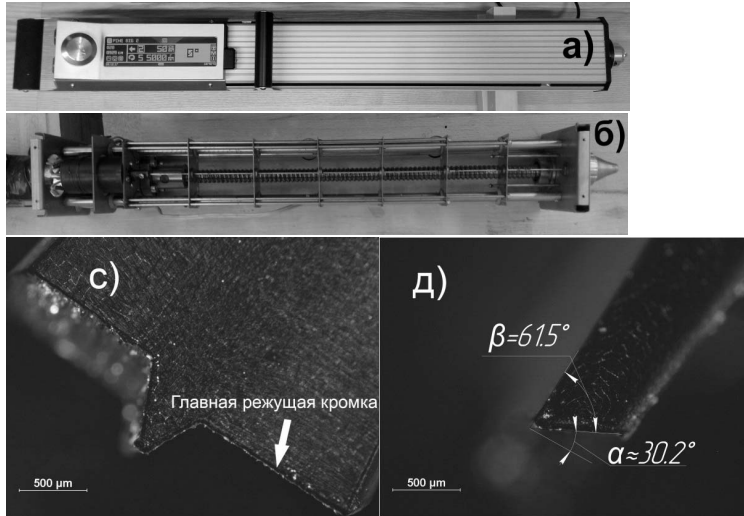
Используемое оборудование и инструмент для измерения сопротивления сверлению: а) устройство для измерения сопротивления сверлению PD-400; б) устройство для измерения мощности сверления ResistYX; с, д) режущая часть бурового сверла, вид спереди и сбоку соответственно, с обозначением статических углов резания: β – заострения и α – заднего угла резания
